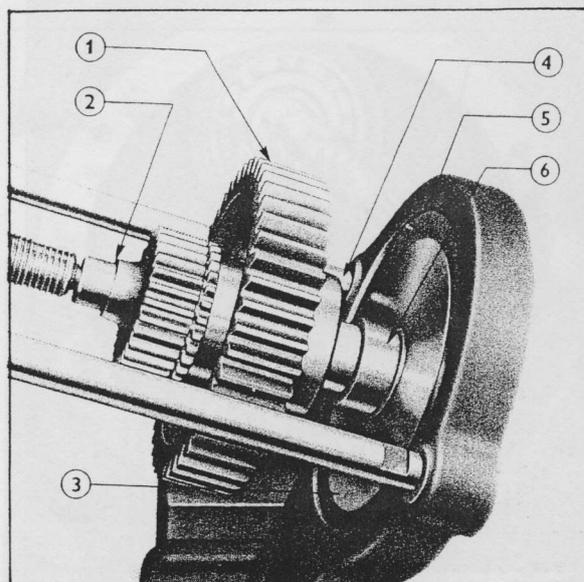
= Repose du Manchon de Joint d'étanchéité d'Arbre de Sortie secondaire
